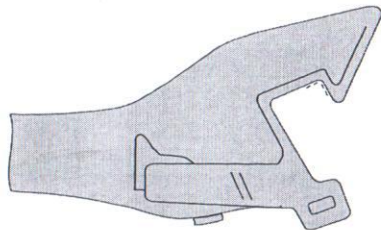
Контроль угла сопряжения боковой и тяговой поверхностей большого зуба
